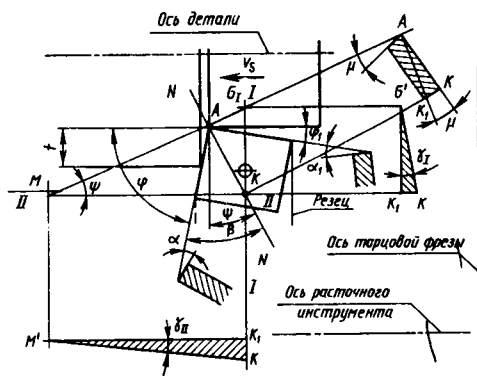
Параметры расположения опорной поверхности многогранной пластины в корпусе инструмента
